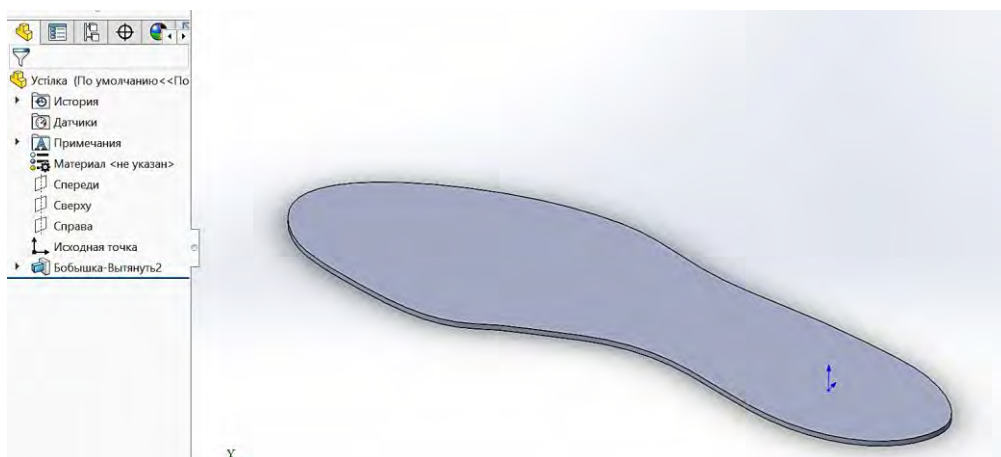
Заготовка на захисний та ізолюючий шари засобу
